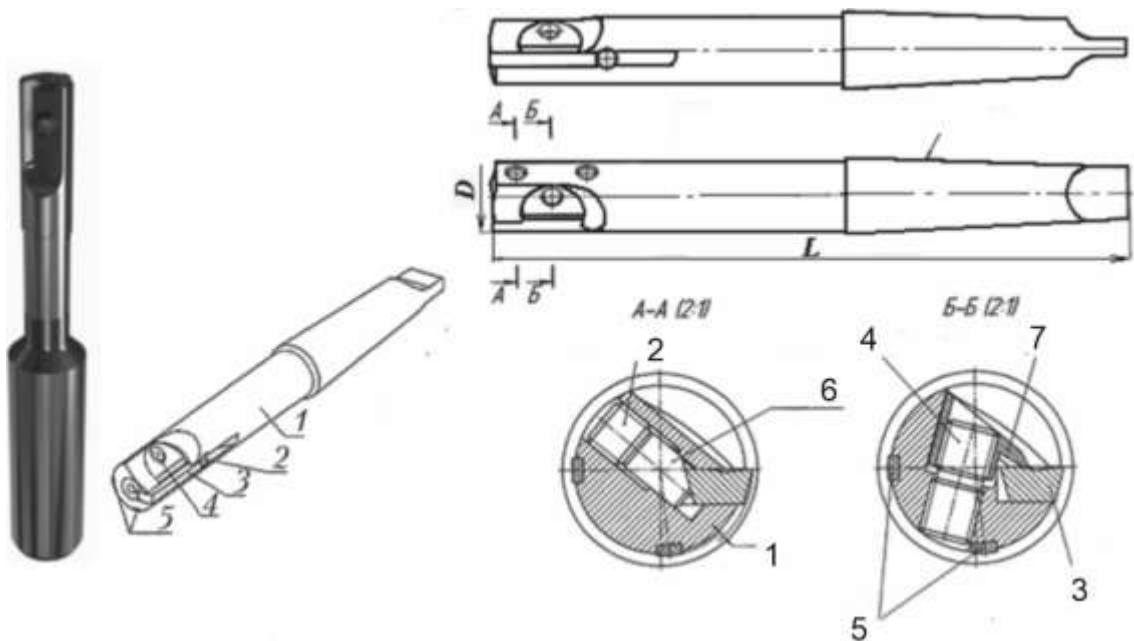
Однолезова розгортка: а-фотографія; б- загальний вигляд; в- конструкція.
